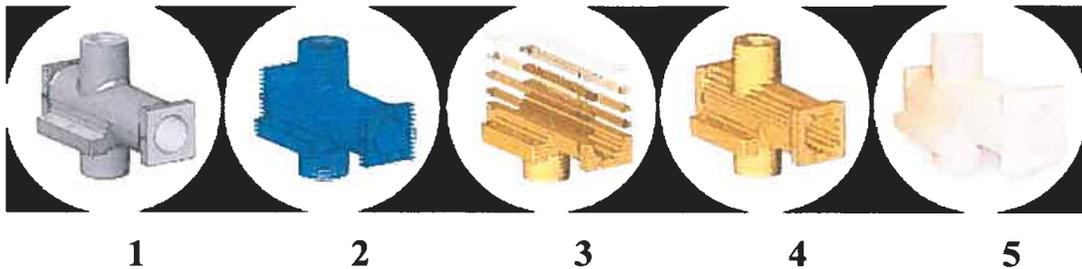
Procédé additif de fabrication d'un prototype.⁷³
